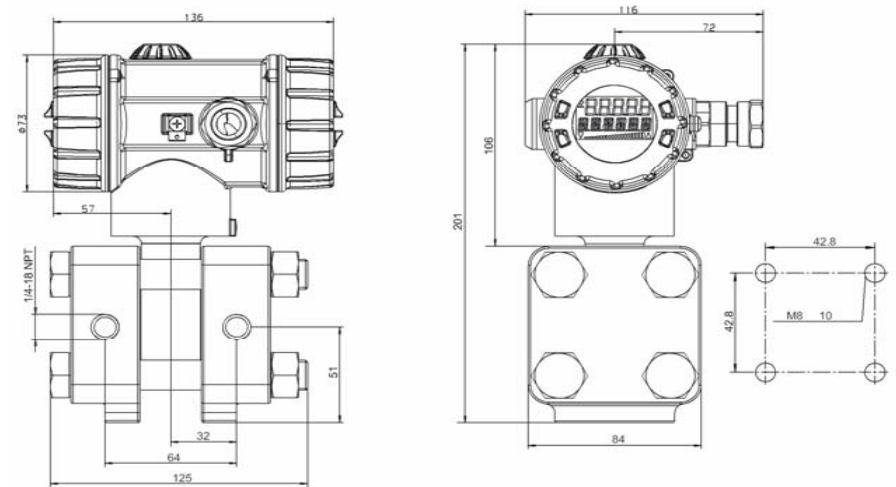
Внешний вид и габаритные размеры преобразователей исполнения для увеличенного номинального давления до 420 bar (код 694)
